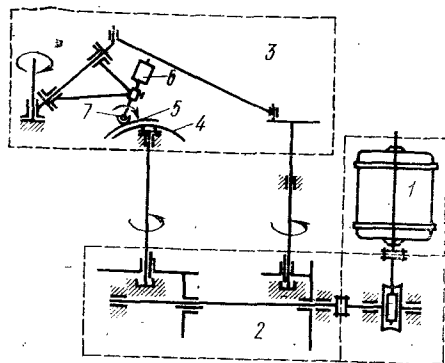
Обобщенная кинематическая схема станков типа ШП
